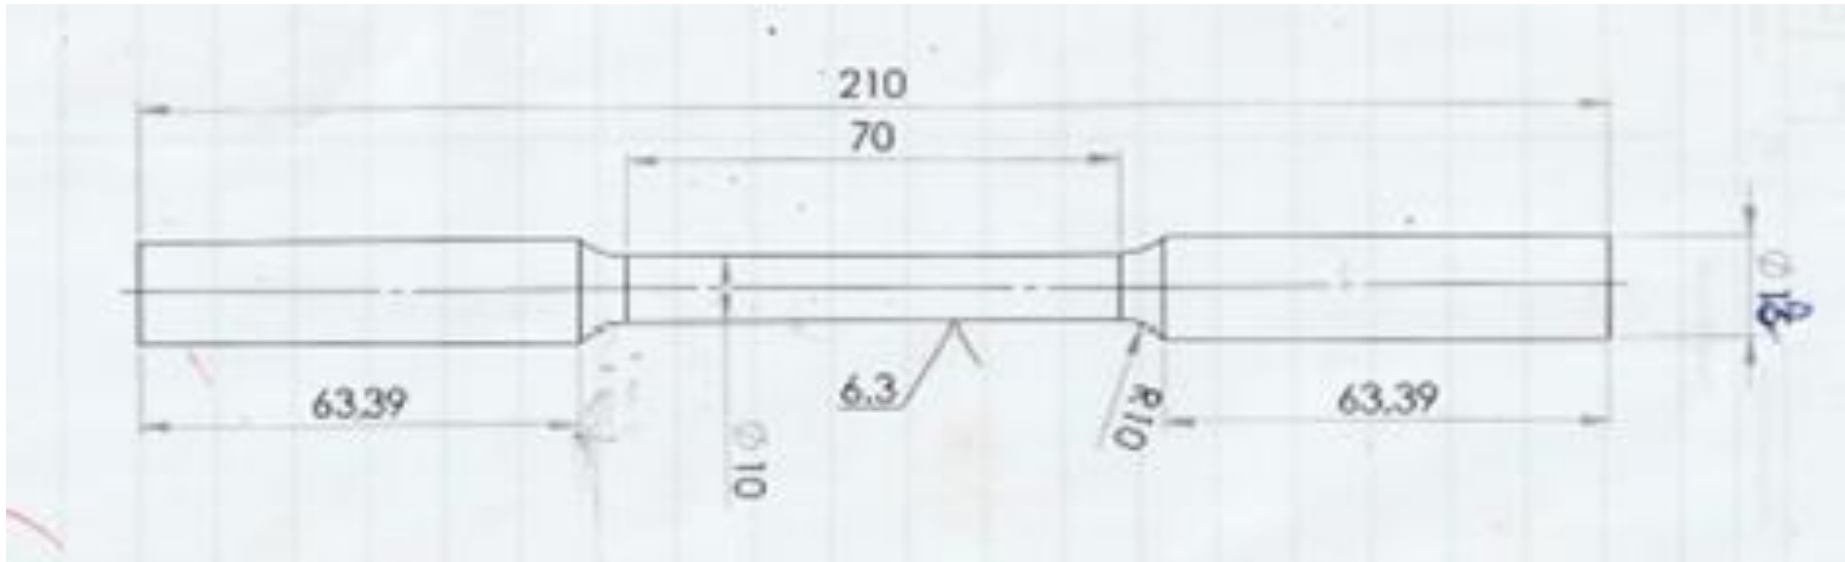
Dimensions technique des éprouvettes destinées à l'essai de traction
